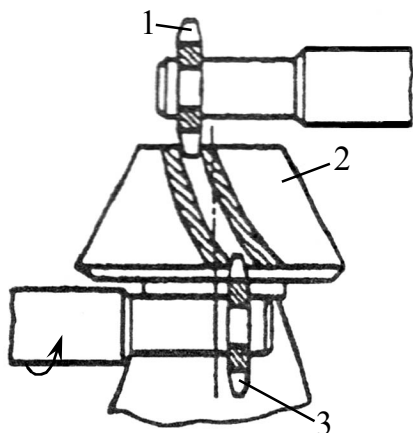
Схема двухстороннего снятия фасок у конического зубчатого колеса: 1, 3 – одновитковые фрезы с разными шагами; 2 – обрабатываемое коническое зубчатое колесо
